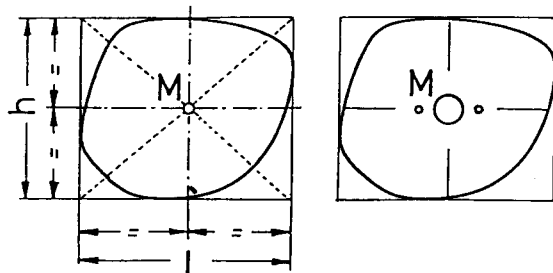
M = centro geométrico de la plantilla = centro de rotación
